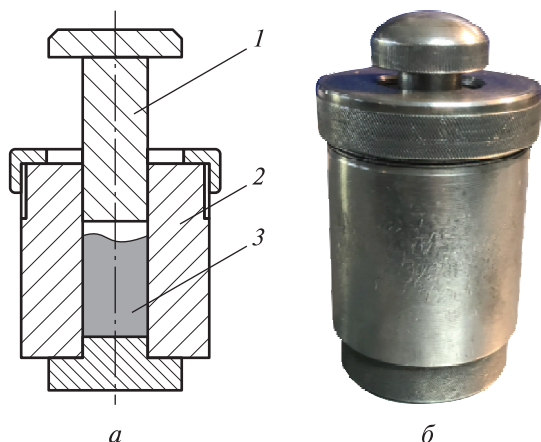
Схема (а) и внешний вид (б) металлической пресс-формы: 1 — шток; 2 — пресс-форма; 3 — засыпка исследуемого состава
